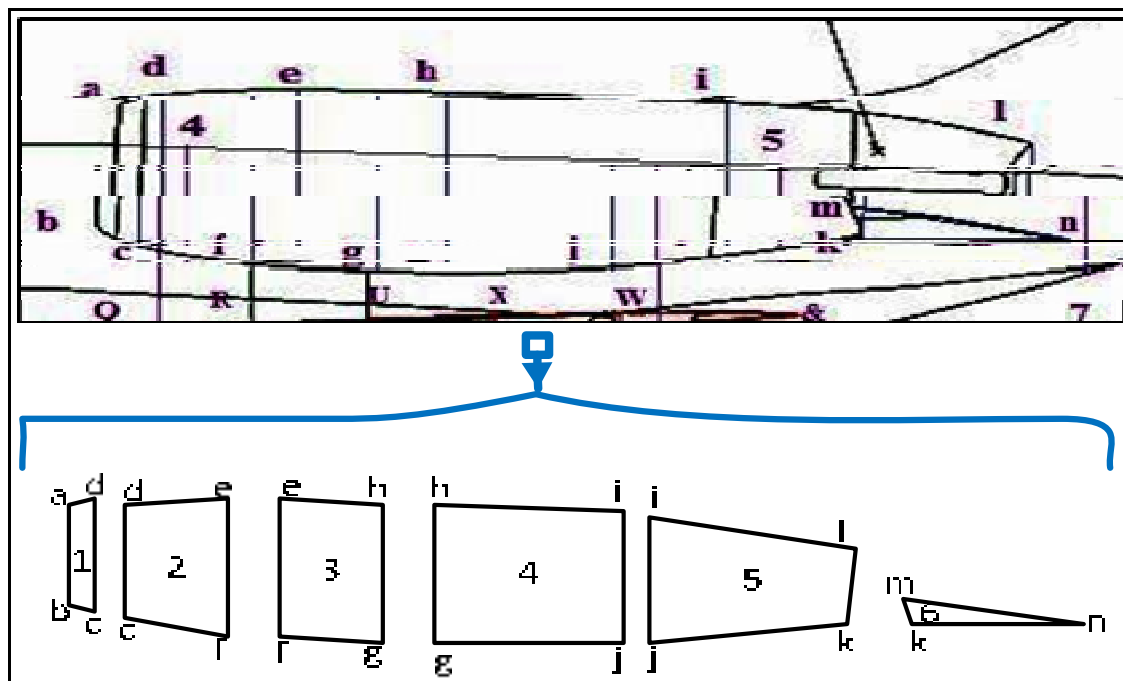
La coupe longitudinale de section de nacelle-moteur
